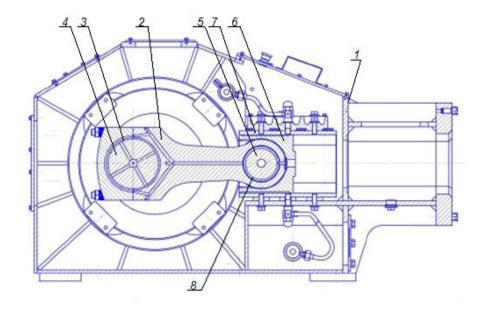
Основные элементы конструкции шатунно-крейцкопфного механизма привода плунжерного насоса высокого давления: 1 — корпус приводной части насоса; 2 — шатун; 3 — вкладыш; 4 — вал кривошипный; 5 — палец шатуна; 6 — крейцкопф; 7 — направляющие; 8 — втулка
